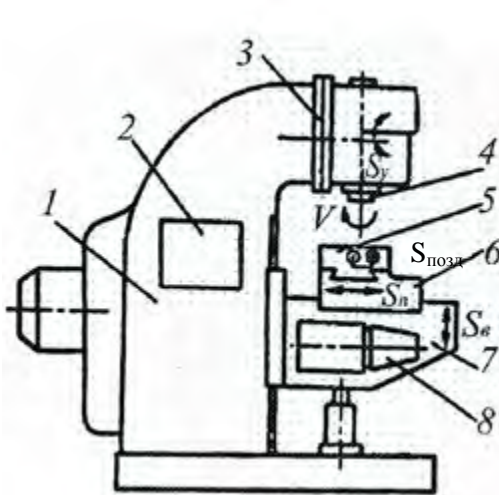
Загальний вид вертикально-фрезерного верстату
